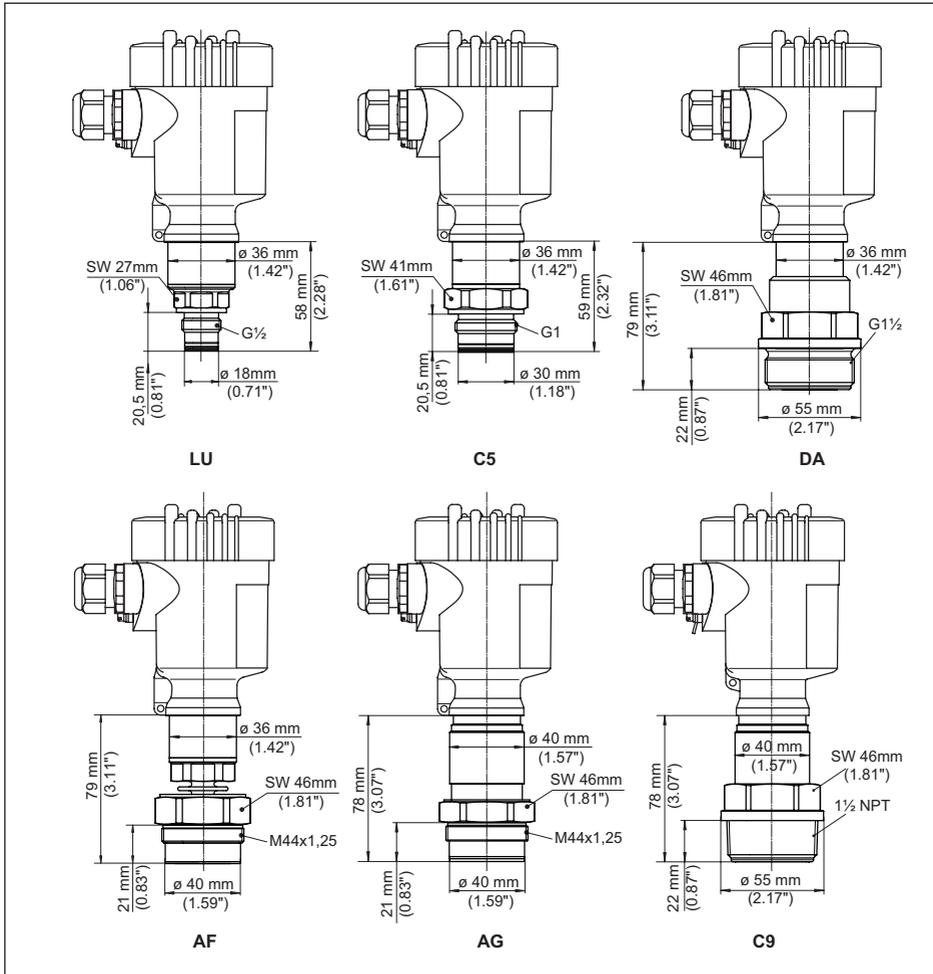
VEGABAR 83, Gewindeanschluss frontbündig
